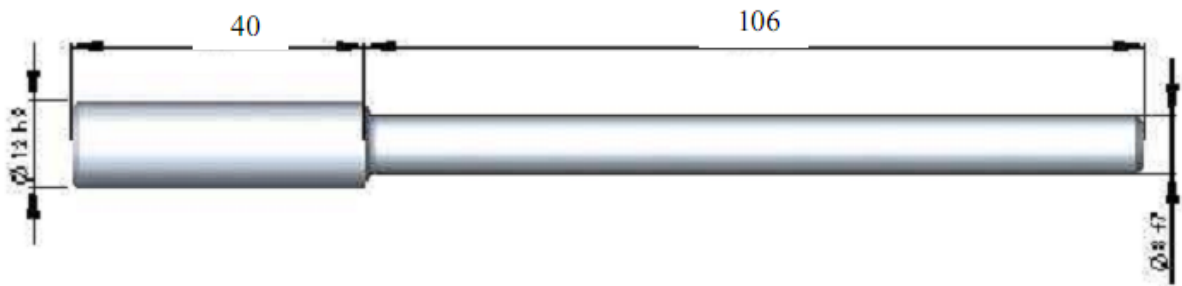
Géométrie de l'éprouvette usinée pour les tests de fatigue [24].
